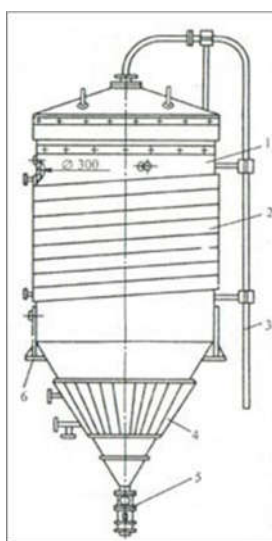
Конструкція циліндрично-конічного апарату
